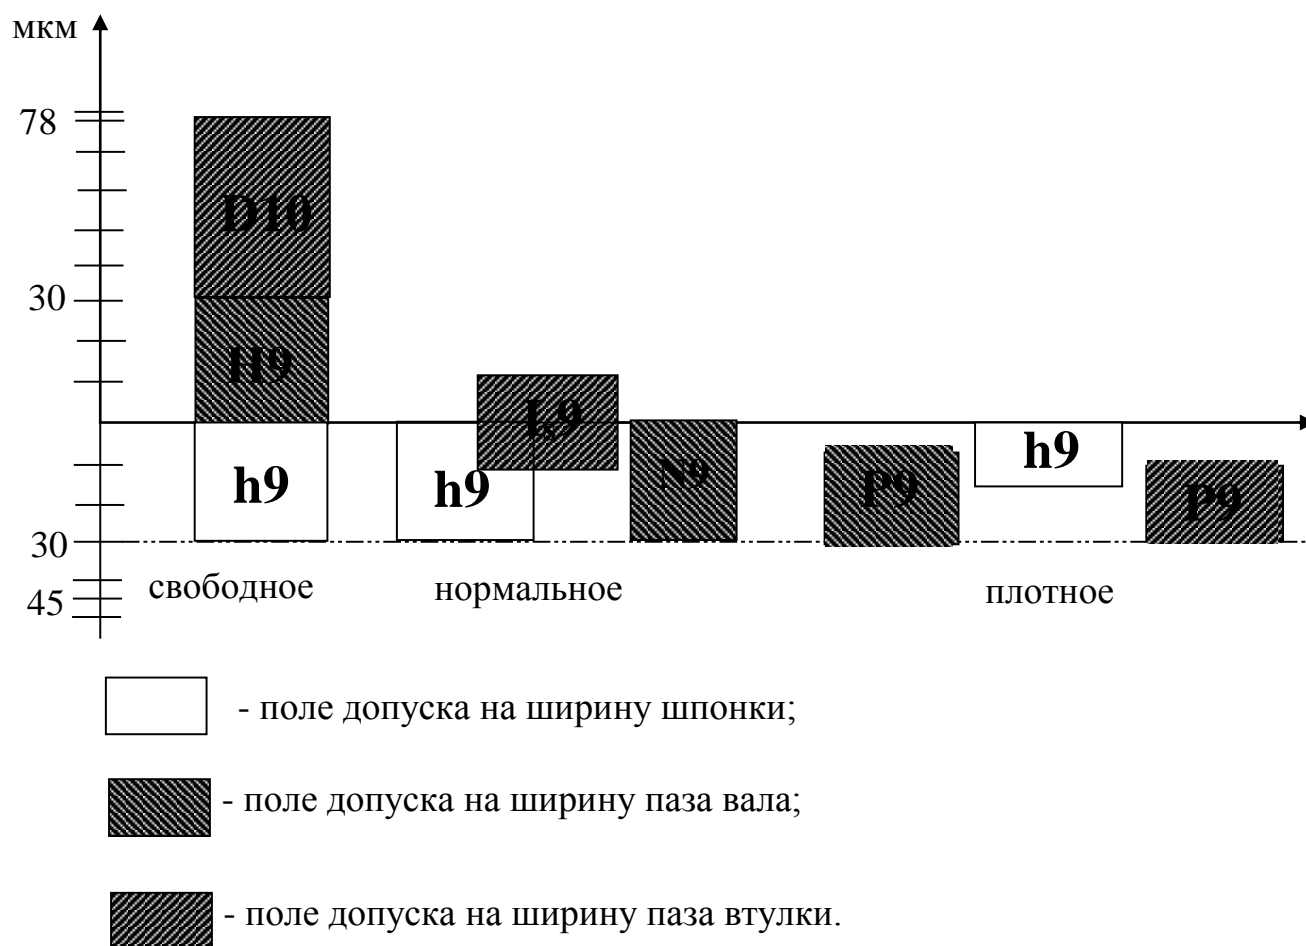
Расположение полей допусков шпоночного соединения
